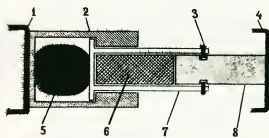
Бампер «Либрети»: 1 — поперечина рамы автомобиля; 2 — корпус; 3 — шпильки, работающие на срез; 4 — бампер; 5 — упругий резиновый элемент; 6 — порывистый штекер; 7 — подвешивающий стержень; 8 — шток.
